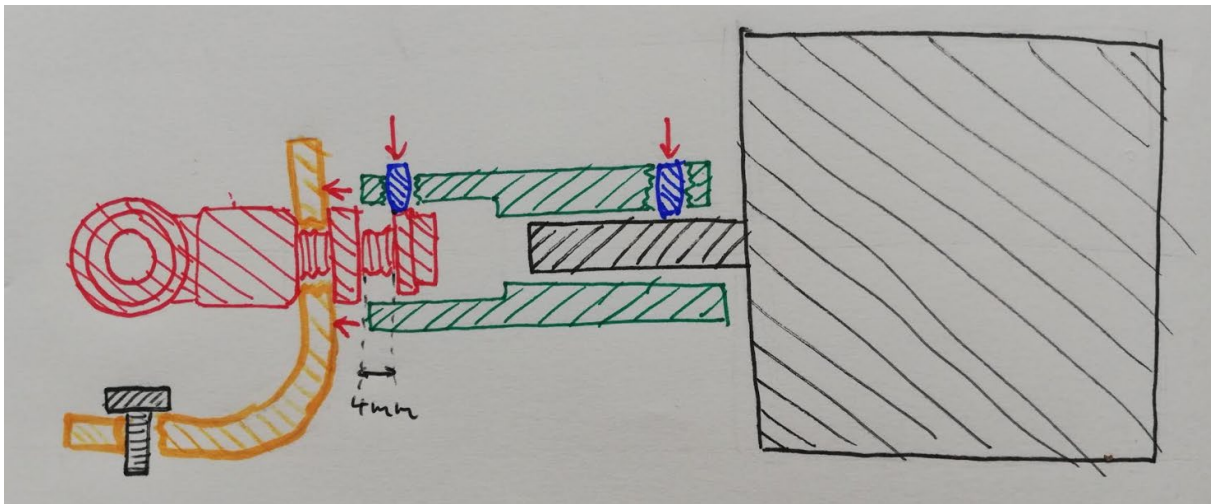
Skizze des Winkels zum Testen des Drosselventils
